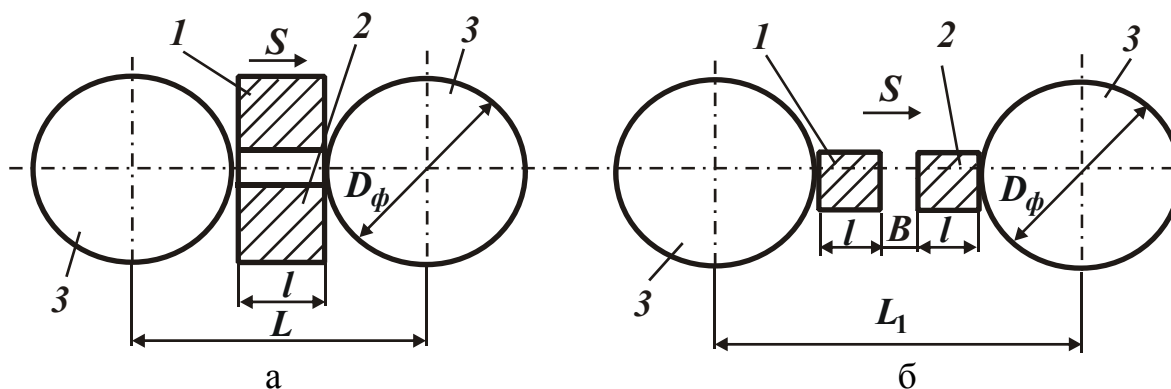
Расположение заготовок в многоместном приспособлении: а - заготовки обрабатываются параллельно; б - заготовки обрабатываются последовательно; D_ϕ - диаметр инструмента (фрезы); l - длина заготовки; B - расстояние между заготовками; L и L_1 - длина перемещения стола соответственно при параллельном и последовательном расположении заготовок.
